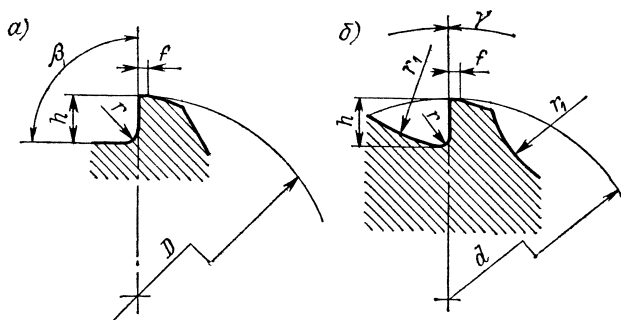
Форма зуба разверток: а — ломаная, выпуклая; б — вогнутая
